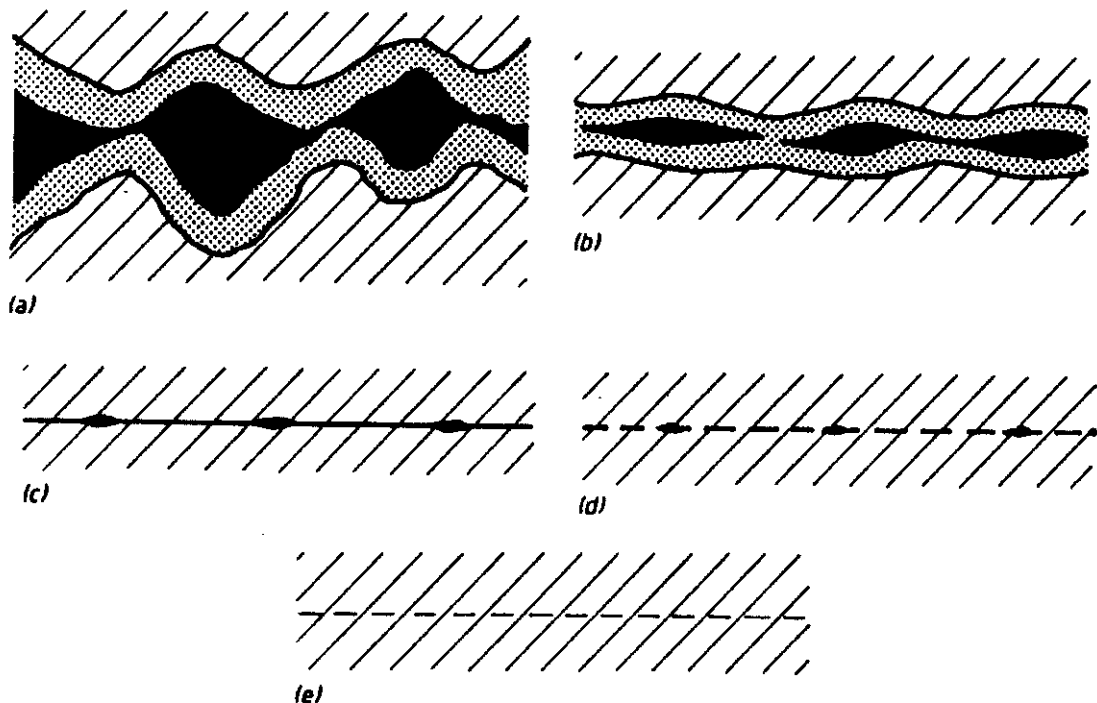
Mecanismo de soldadura por difusión (212)
